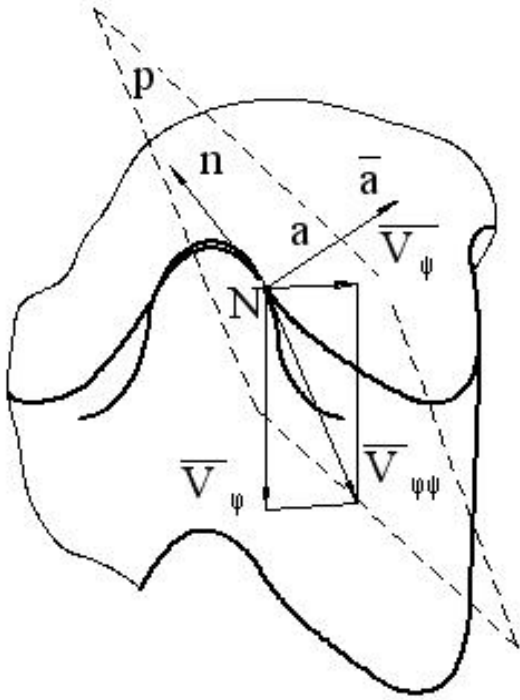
Схема расчета геометрической основы математической модели обработки зубчатых колес передачи инструментами червячного типа
